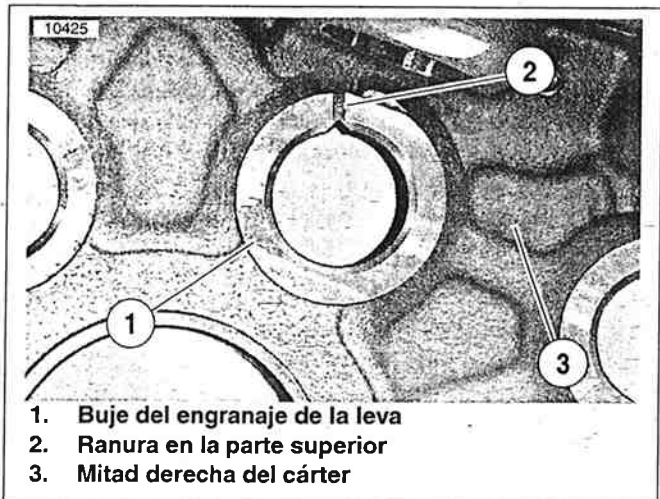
Bujes del engranaje de la leva instalados en el cárter
